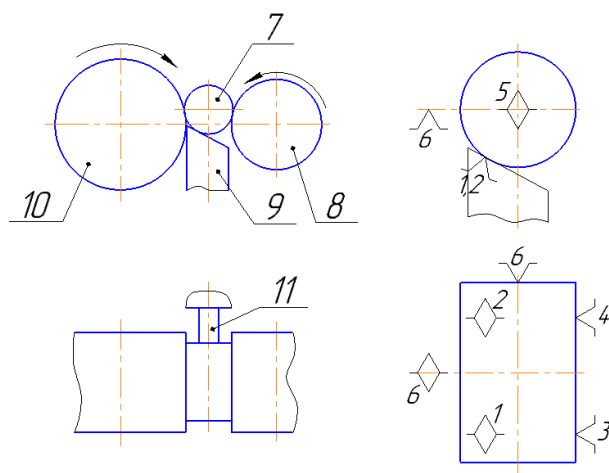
Установка заготовки по обрабатываемой поверхности при бесцентровом врезном шлифовании: 1–6 – опорные точки; 7 – заготовка; 8 – ведущий круг; 9 – опоры; 10 – шлифующий круг; 11 – продольный упор
